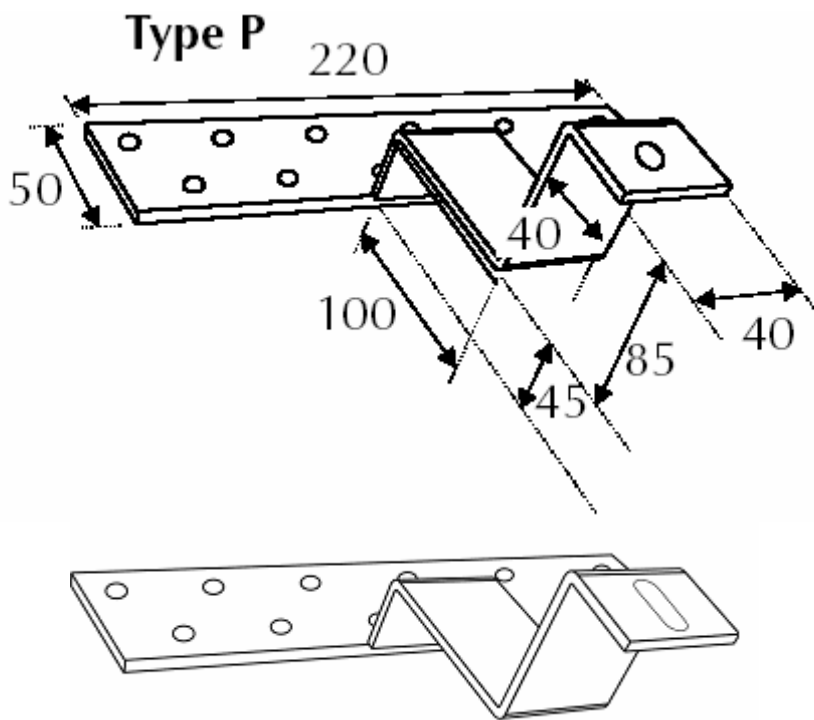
Patte de fixation de type P pour toiture inclinée, tuiles mécaniques
